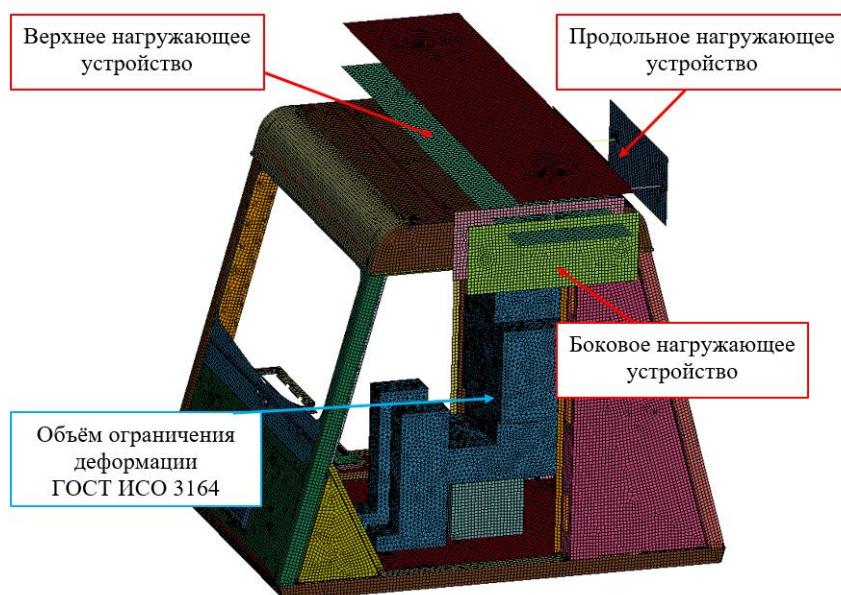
Конечно-элементная модель кабины карьерного самосвала с нагружающими устройствами
